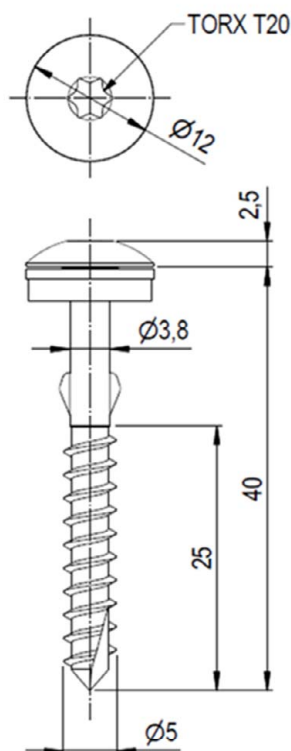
Holzschraube SFS intec 5,0x40 K12 mit Dichtung selbstbohrende
